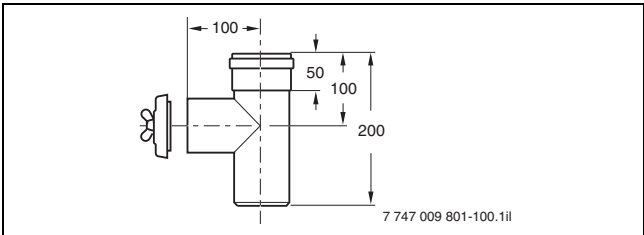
Inspektions-T-Stück für Abgasleitung im Schacht (Maße in mm)
